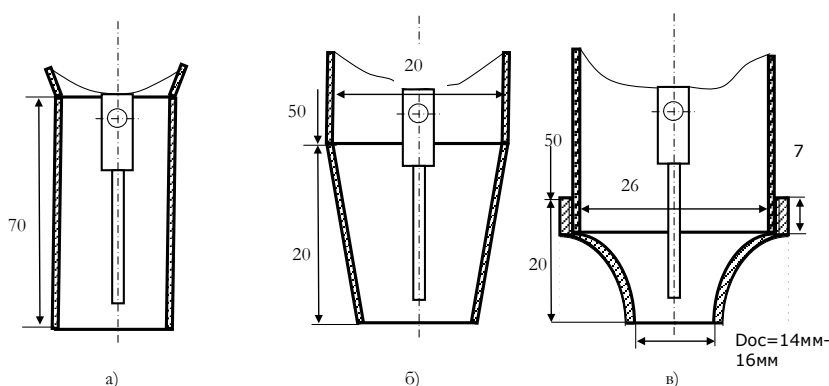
Конструкции сопел сварочных горелок
